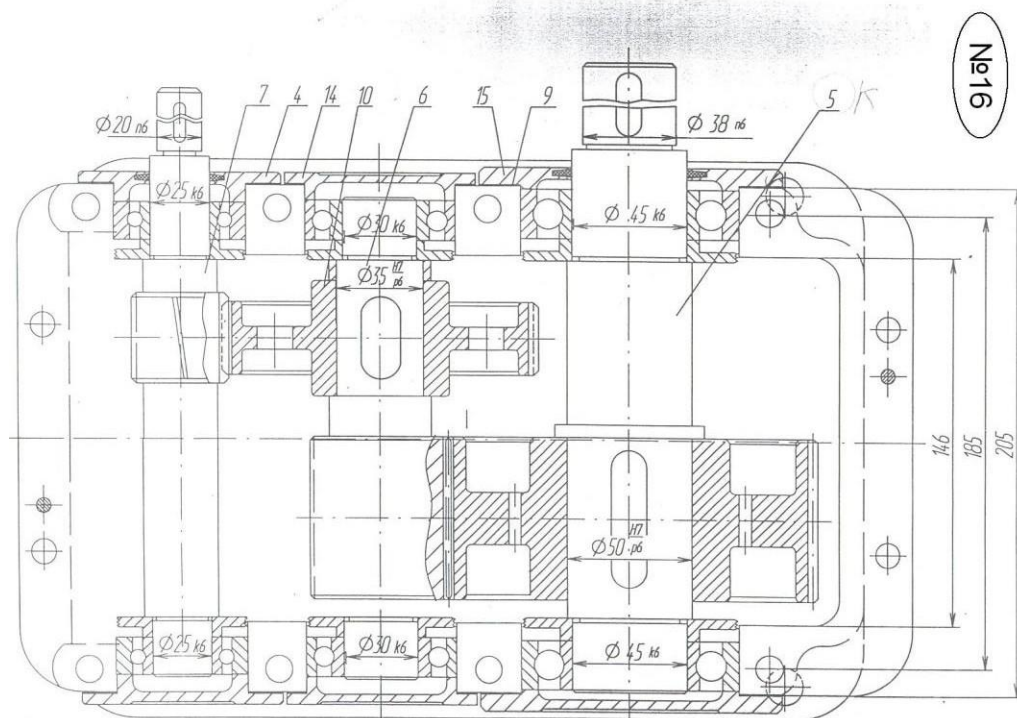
Двухступенчатый коническо-цилиндрический редуктор
